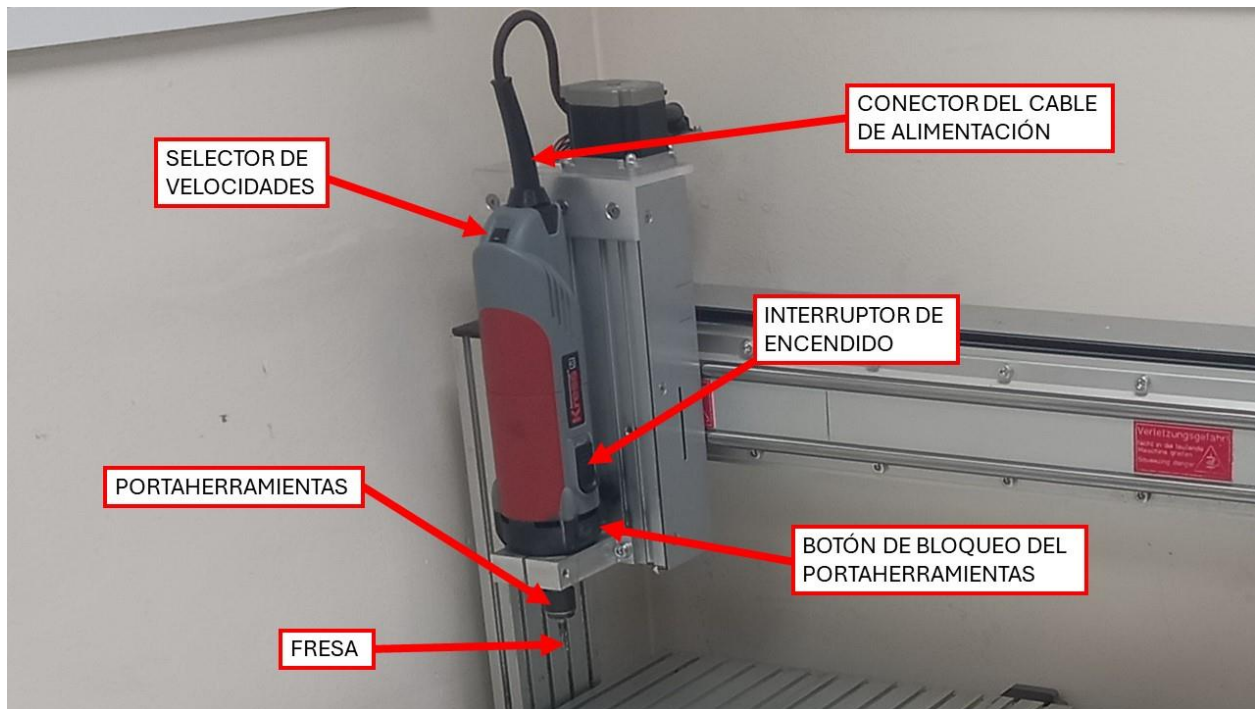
Motor fresador instalado en su brida y con una fresa en el portaherramientas. (Elaboración propia)
